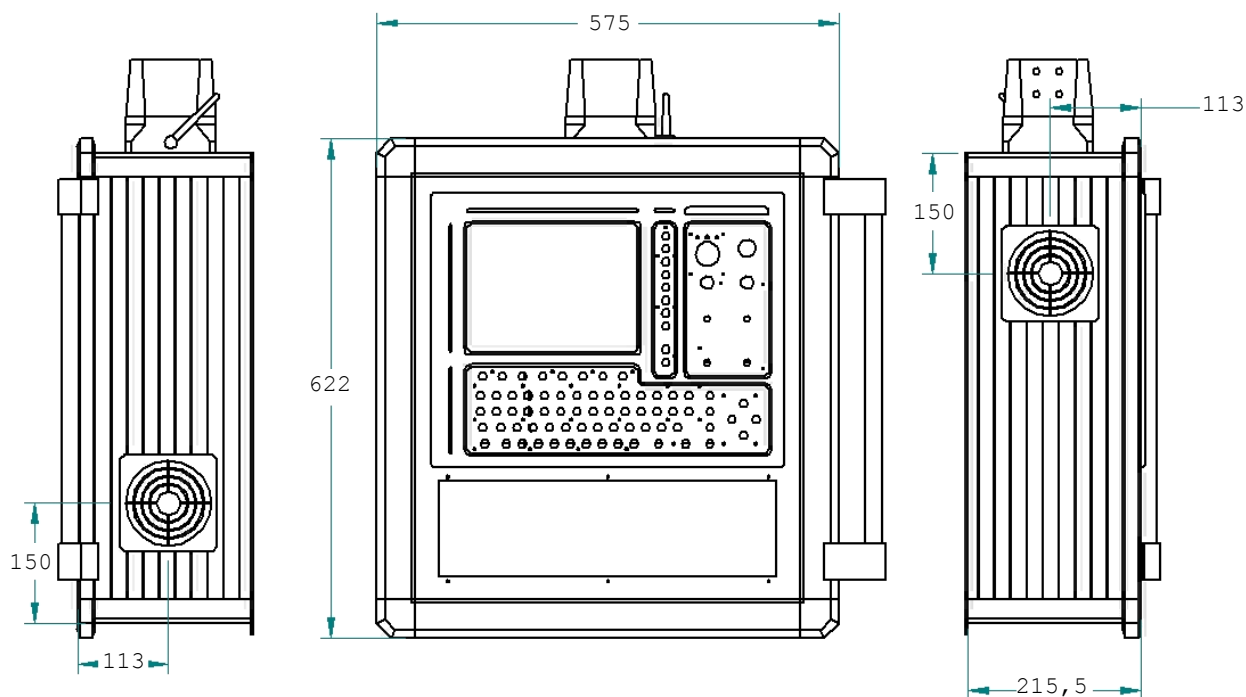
Габаритные размеры кожуха для УЧПУ NC-220.
